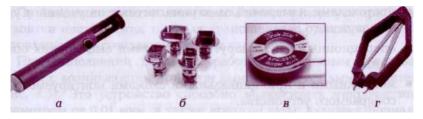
Монтажное оборудование: а -оловоотсос; 6 -насадки к фену; 8 -оплетка; r -экстрактор
